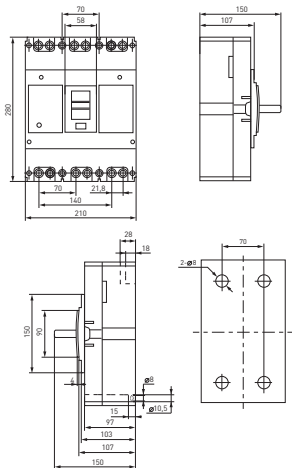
Габаритные и установочные размеры автоматических выключателей
